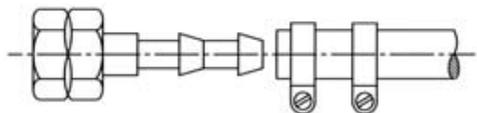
Schlauchanschlüsse für Flüssiggasanlagen – bevorzugt sollen fest eingebaute Anschlüsse verwendet werden
